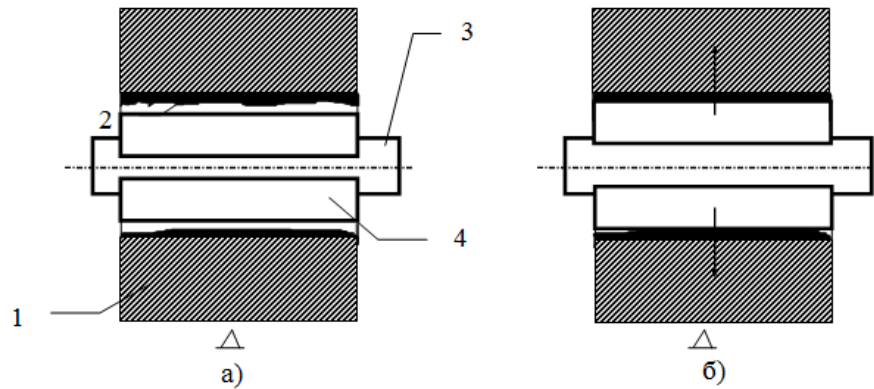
Центрирующее приспособление для склеивания корпуса водяного насоса и подшипников 304, 305 с валом
